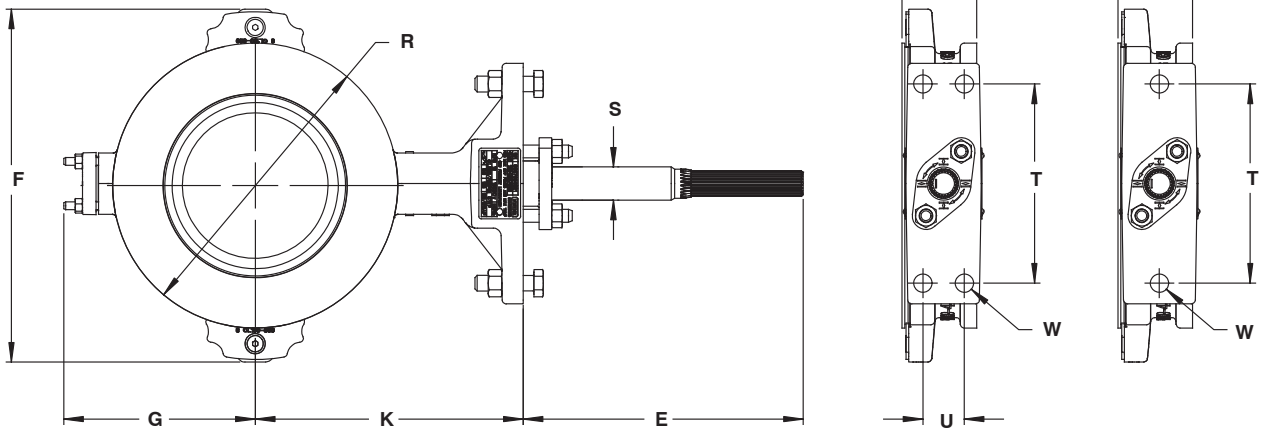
Размеры затвора 8580 (бесфланцевый корпус)
